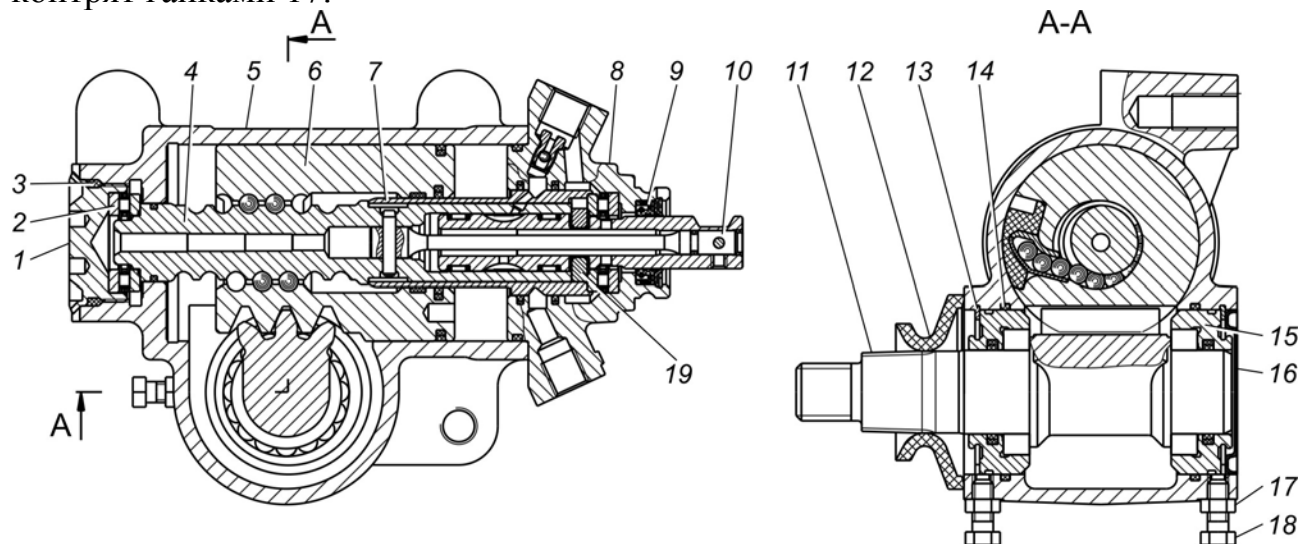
Рулевой механизм с гидроусилителем: 1 – регулировочная гайка; 2 – подшипник; 3 – уплотнительное кольцо; 4 – винт; 5 – картер; 6 – поршень-рейка; 7 – гильза; 8 – корпус распределителя; 9 – манжета; 10 – вал-золотник; 11 – вал-сектор; 12 – защитная муфта; 13 – стопорное кольцо; 14 – уплотнительное кольцо; 15 – наружное кольцо; 16 – защитная крышка; 17 – гайка; 18 – болт; 19 – упор
